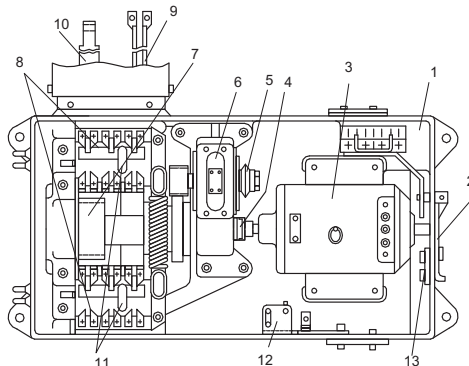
Стрілочний привод типу СП-6 (вигляд зверху)
